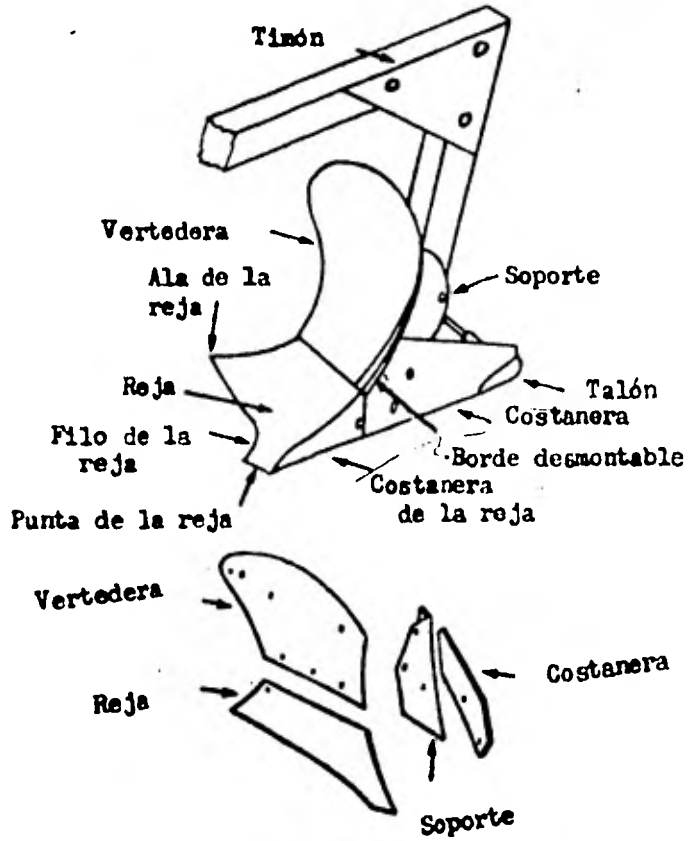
Conjunto y despiece de un cuerpo de arado
